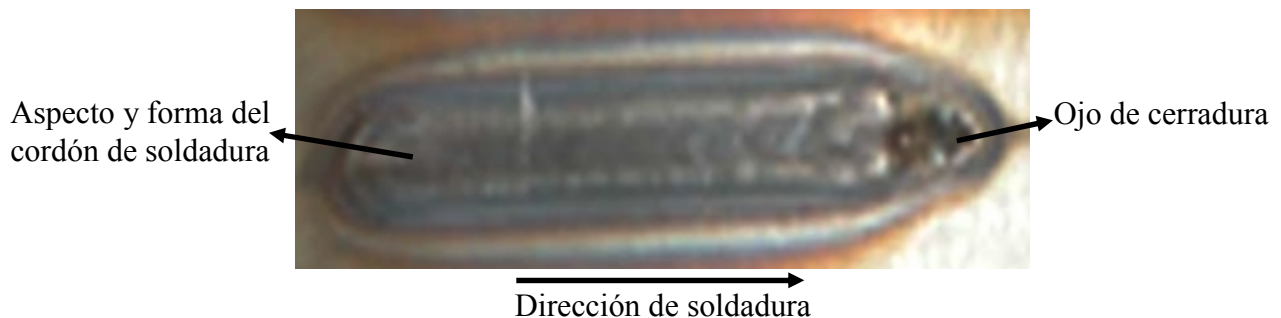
Aspecto superficial de la soldadura y el ojo de cerradura
